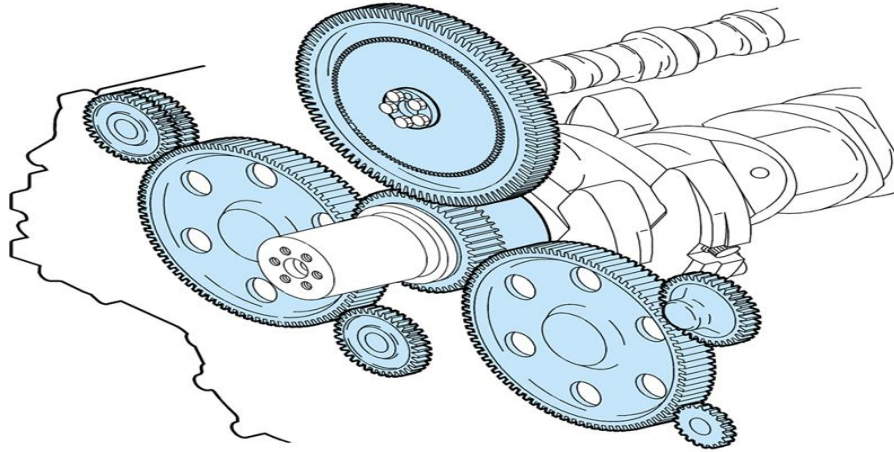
Tren de engranajes del motor MTU S4000 G81.
